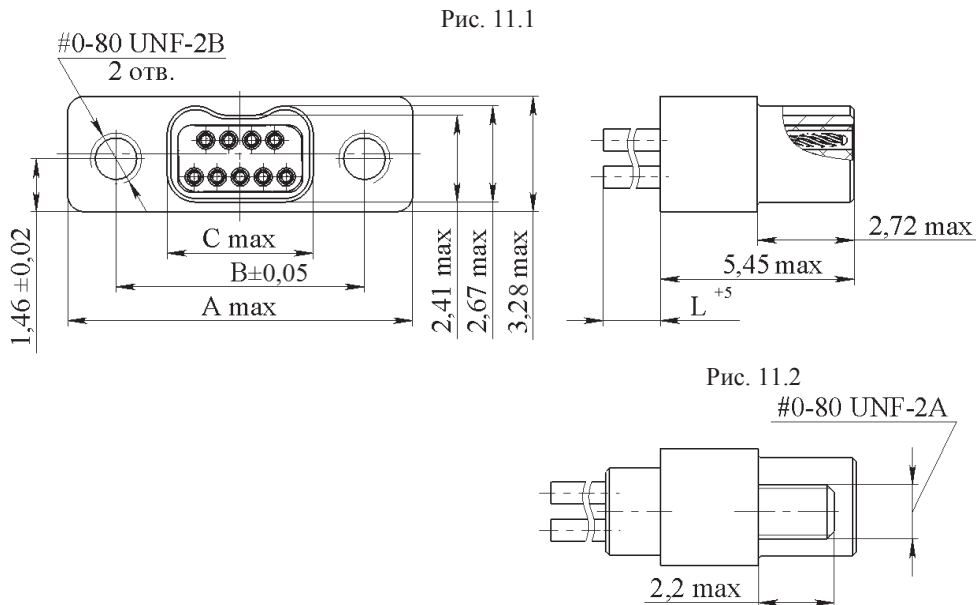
Соединитель СП450-01...2...Ш1...
